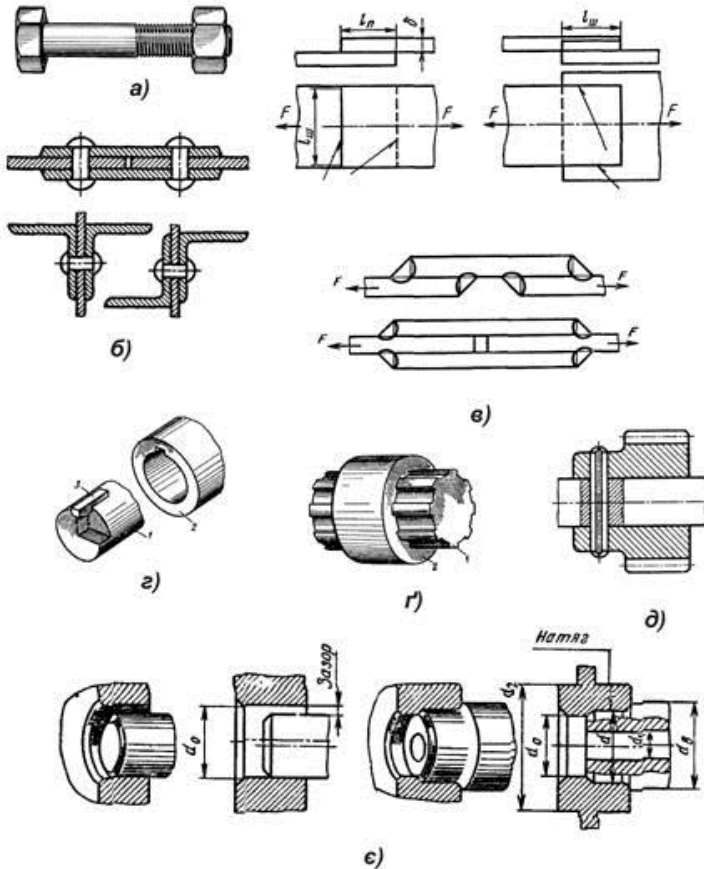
З'єднання деталей машин: а) різьбове, б) заклепкові, в) зварні, г) шпонкове, д) штифтове, е) з'єднання з натягом
